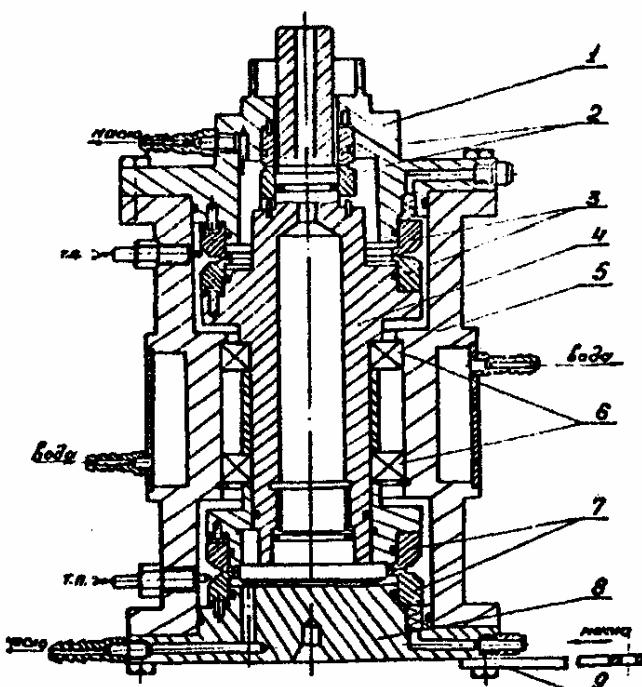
Рабочий узел стенда для испытания торцевых уплотнений: 1 — верхняя крышка; 2 — запирающее торцевое уплотнение; 3 — верхнее торцевое уплотнение; 4 — вал; 5 — корпус; 6 — шарикоподшипник; 7 — нижнее торцевое уплотнение; 8 — нижняя крышка; 9 — рычаг.
